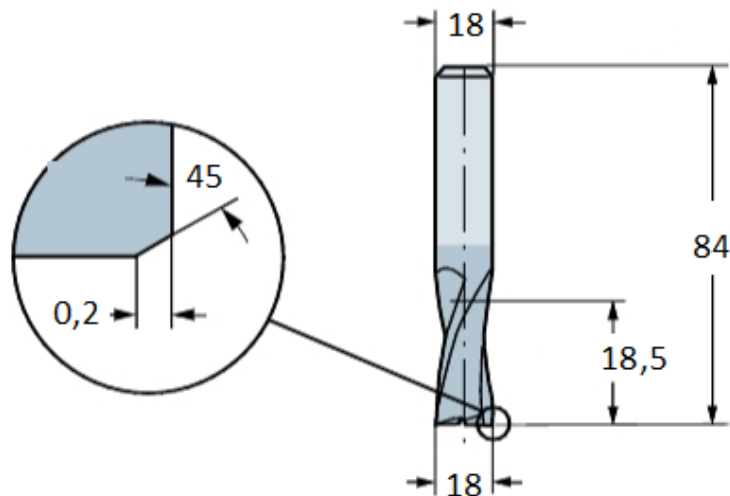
Концевая фреза Sandvik Coromant CoroMill 1P220-1800-XA 1630
